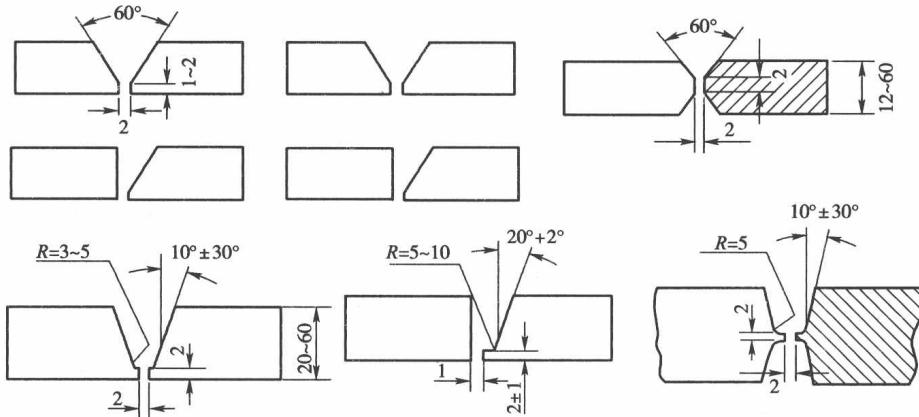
对接焊缝各种坡口型式(尺寸单位:mm)
